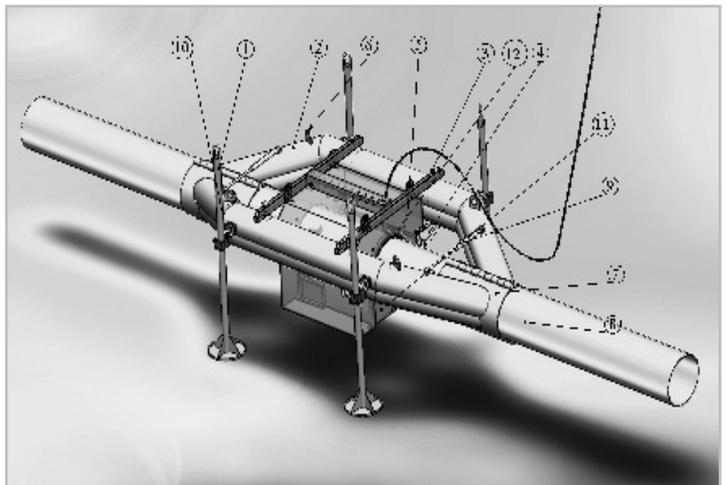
Общий вид подводного сварочного комплекса: опора – 1; установочная рама – 2; опорная балка – 3; откидной упор – 4; корпус кессона – 5; грузовая проушина – 6; трубный захват – 7; трубопровод – 8; гидронатяжитель – 9; герметизирующие створки – 10; камера для сухой сварки – 11; пневматическое уплотнение – 12.
